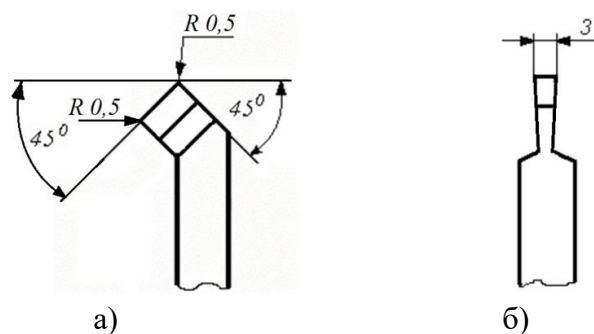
Схемы резцов: а) резец токарный проходной с отогнутой головкой и пластиной из твердого сплава Т15К6; б) резец токарный отрезной с пластиной из твердого сплава Т15К6
